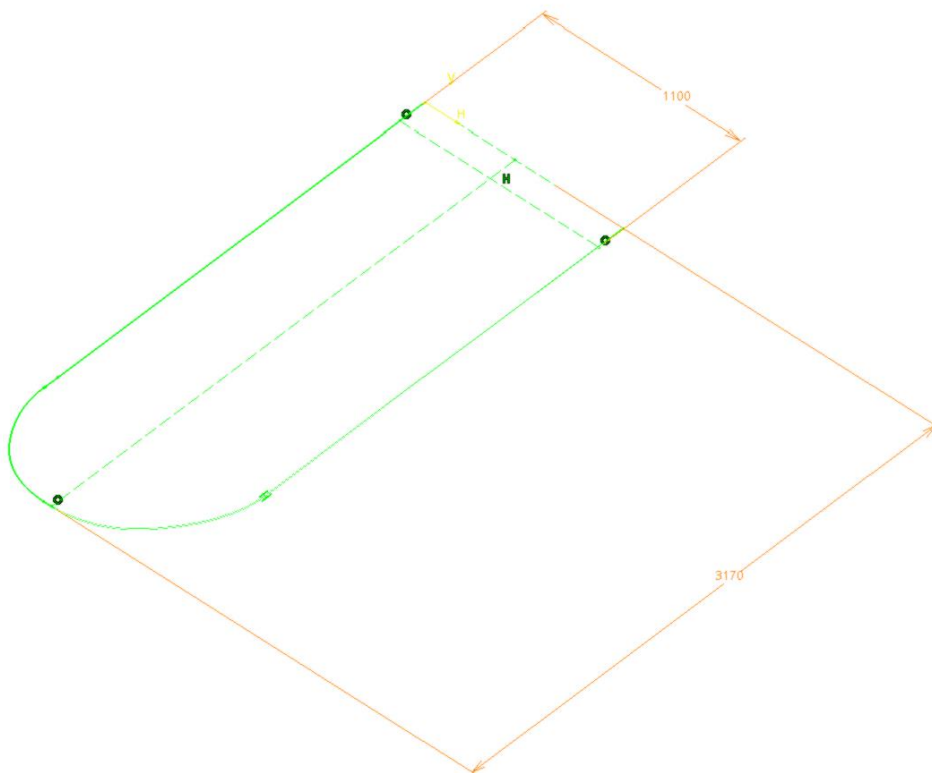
Sketch obtenido de la forma en planta del ala inferior
